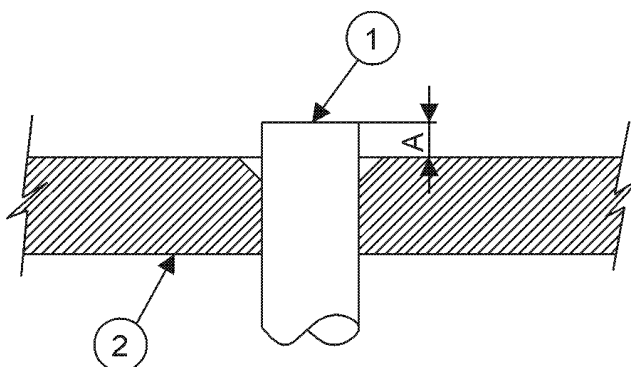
Einsetzen des Rohrs in das Aufweitwerkzeug
